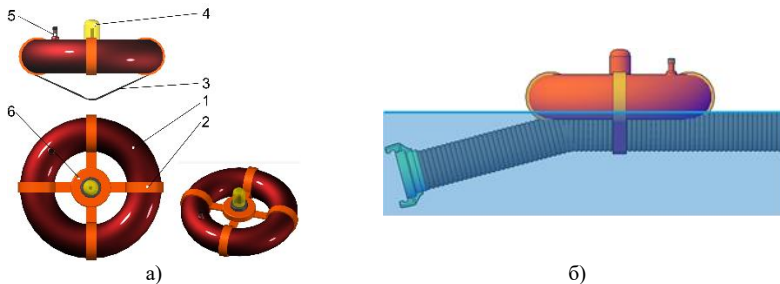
Поплавковое устройство: а – конструкция устройства; б – устройство с прикрепленным всасывающим рукавом: 1 – камера резиновая; 2 – ребра жесткости; 3 – хомут; 4 – фонарь; 5 – ниппель.
